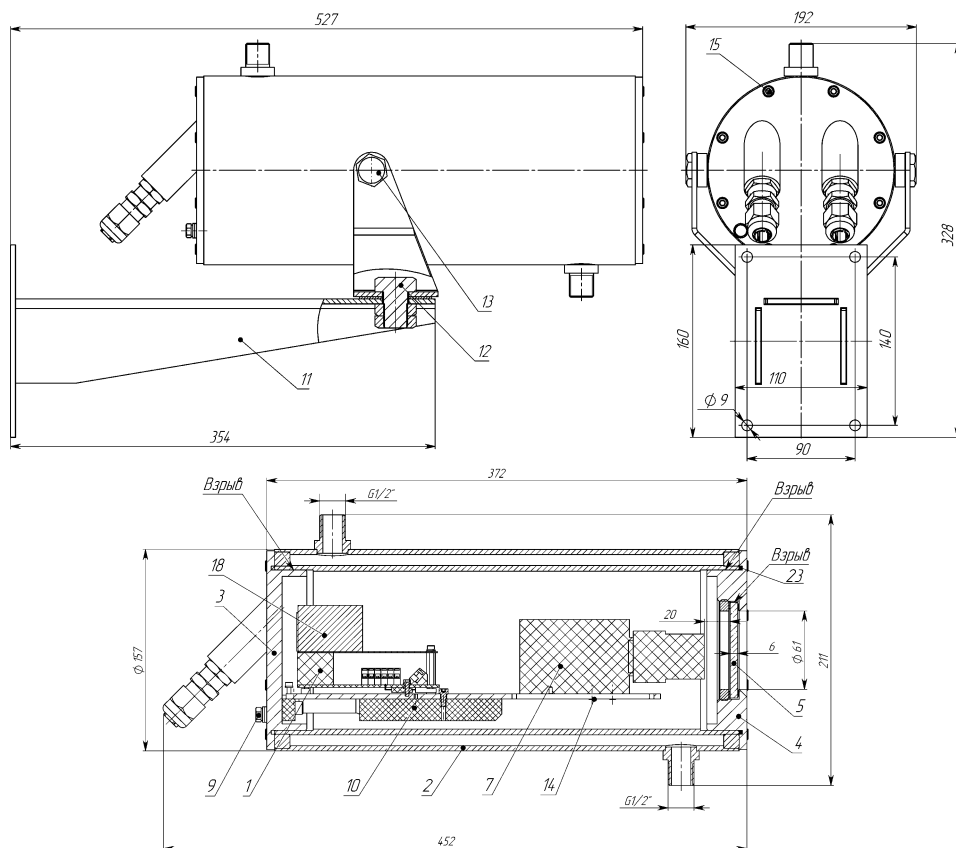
Внешний вид термокожуха ТВК-07-В
